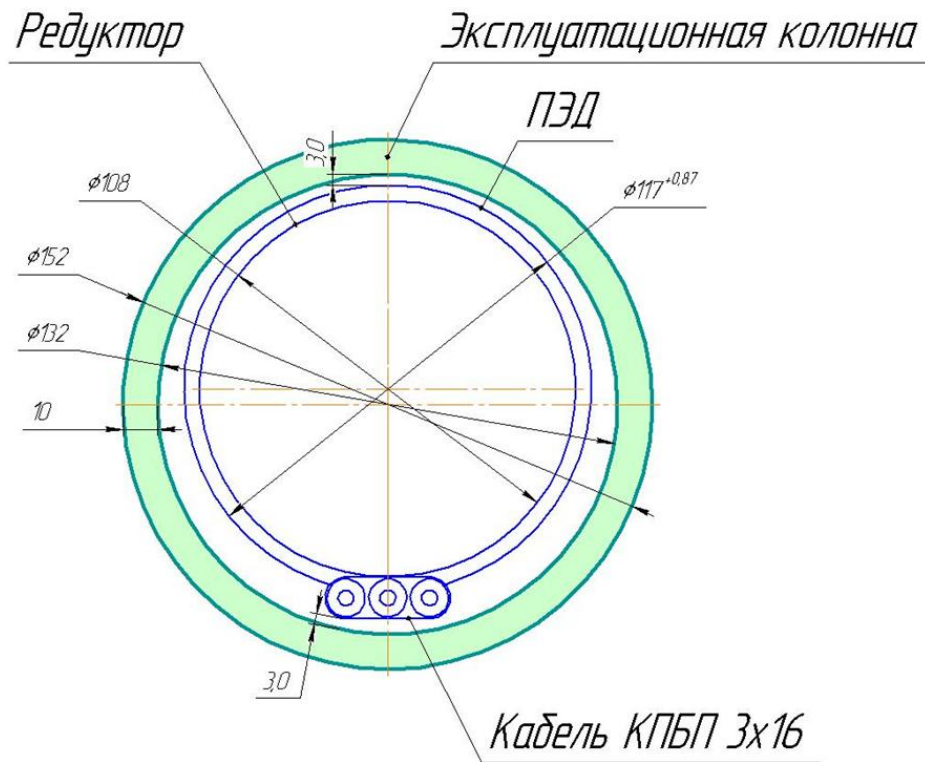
Поперечный габарит установки на базе ГМПР
